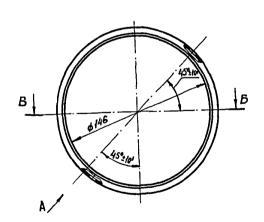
Корпус (3.680.013CB) (в сборе с корректором) Поз.2. Рис.1
